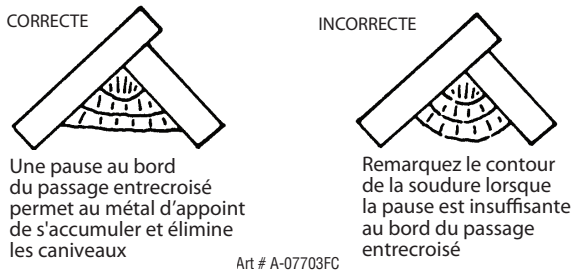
Exemples de soudure d'angle verticale
